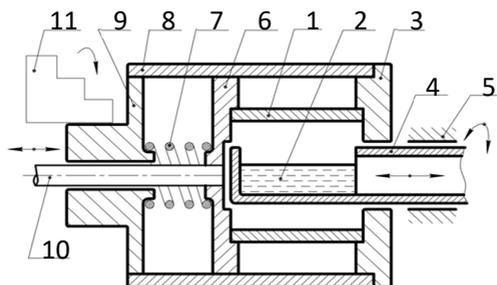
Схема центробежного литья: 1 – форма; 2 – металл; 3 – диск; 4 – трубка; 5 – направляющие; 6 – нажимной диск; 7 – пружина; 8 – кожух; 9 – корпус; 10 – шток; 11 – кулачки
